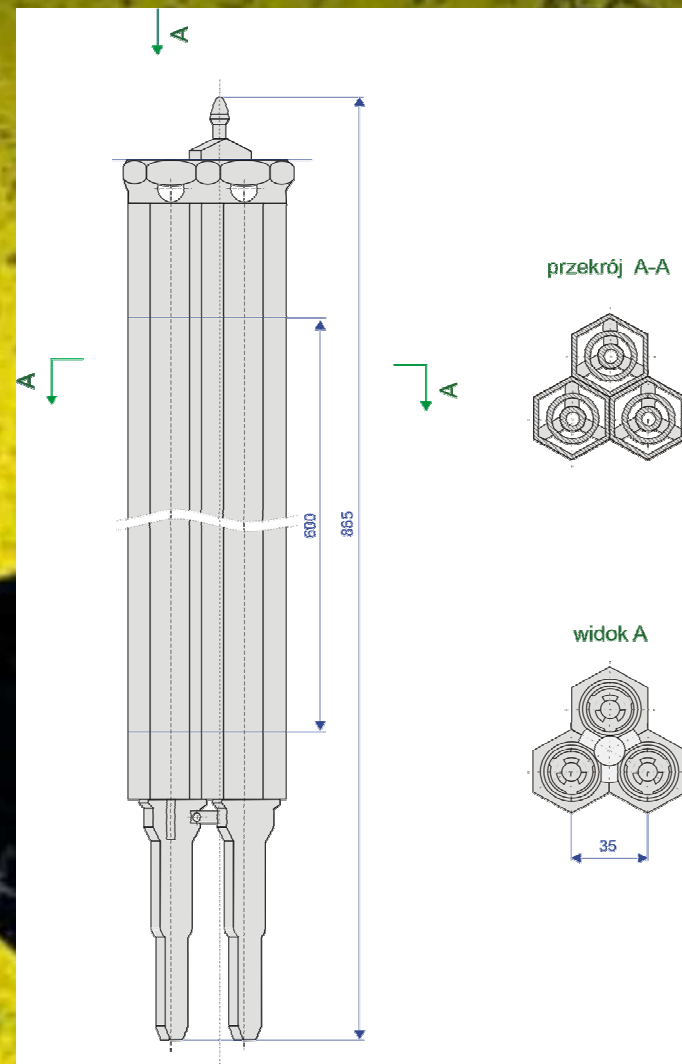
WIADERKO NA WYPALONE PALIWO EK-10
